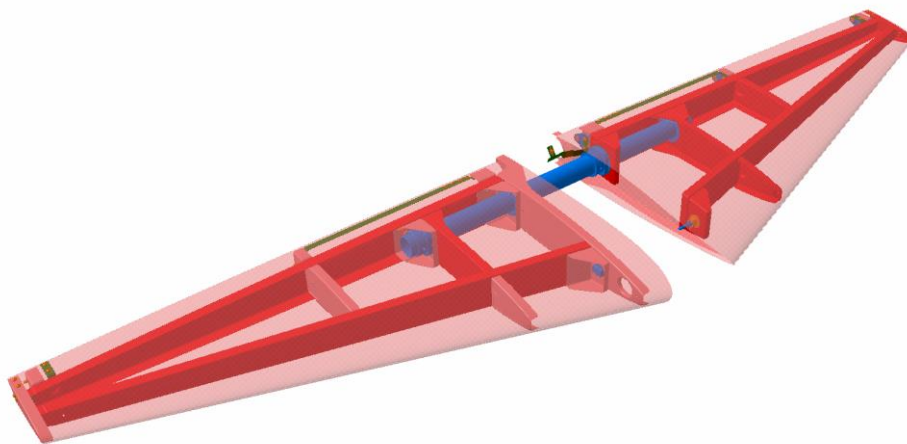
GEOMETÍA DETALLADA DEL EMPENAJE HORIZONTAL.
